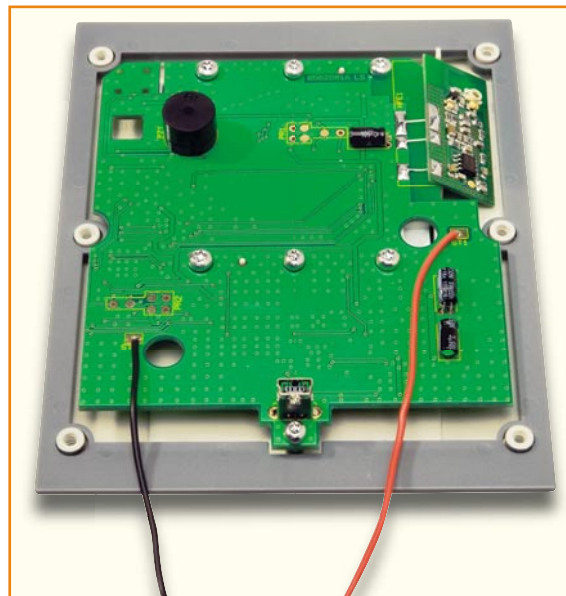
Detailansicht zum Anlöten der Batterie Anschlussleitungen
